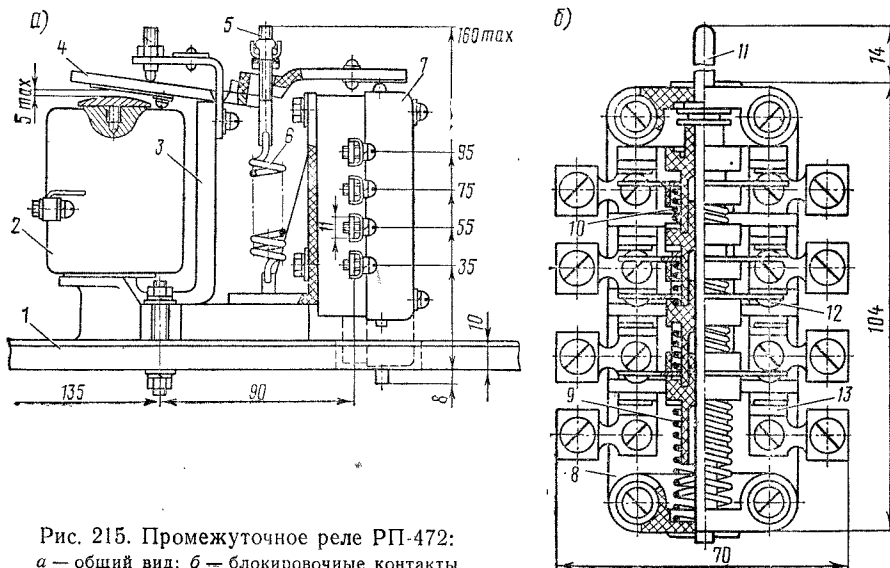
Промежуточное реле РП-472: а — общий вид; б — блокировочные контакты
